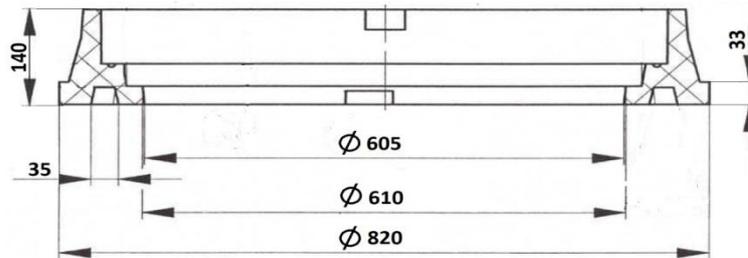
Габаритные размеры корпуса люка ППЛ.
